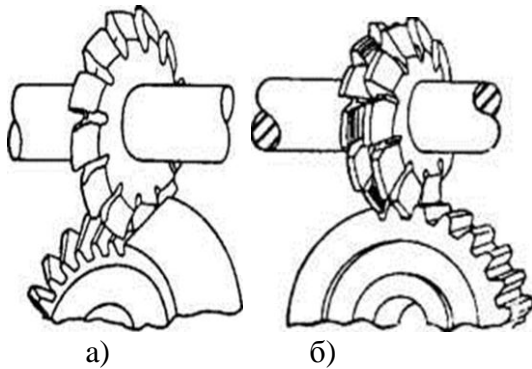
Схемы нарезания дисковыми фрезами конических (а) и цилиндрических (б) зубчатых колес
